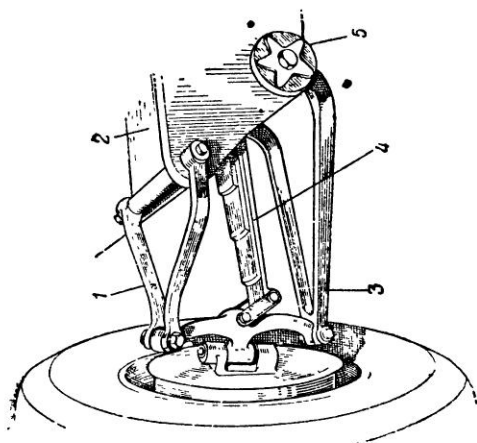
Независимая подвеска с поперечной рессорой и двумя выльчатыми рычагами:
